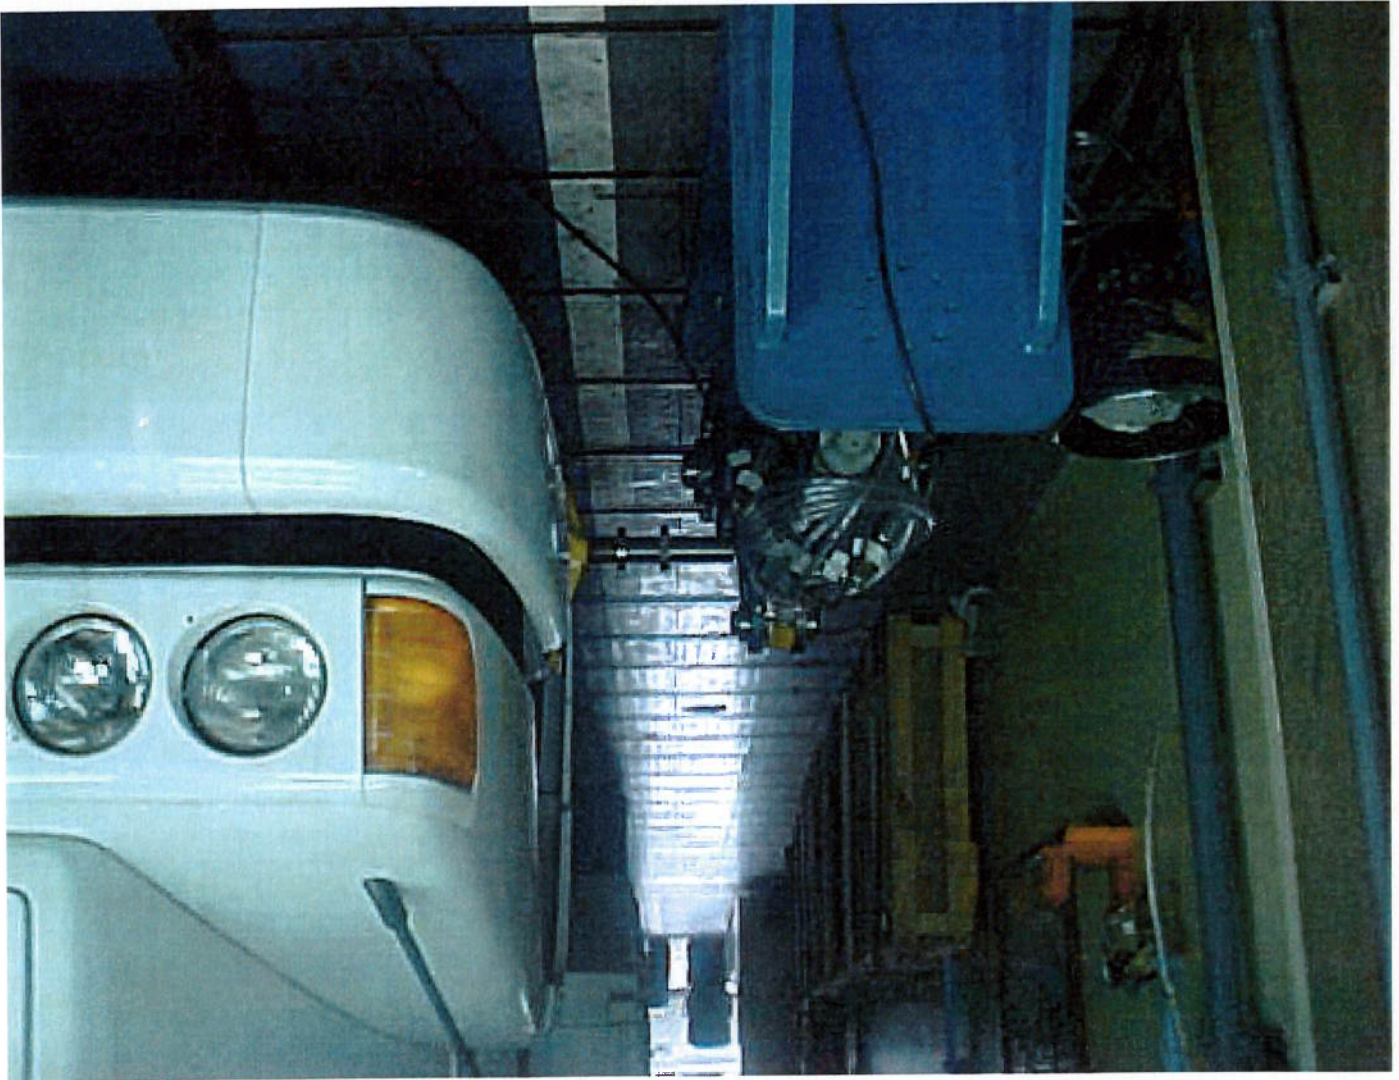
CAMINHÃO FIXADO PELO LADO DIR. NO DISPOSITIVO
